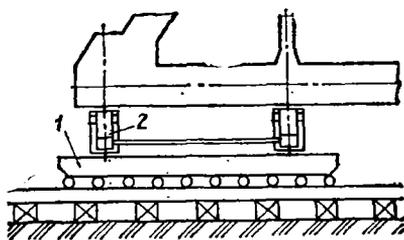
Перекаточная каретка 1 с гидравлическими домкратами 2
